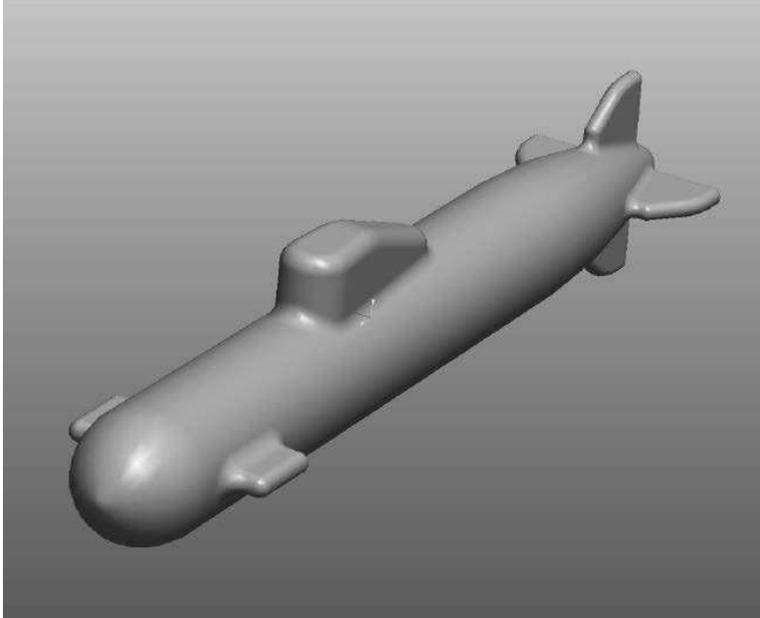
Geometrie des U-Bootes in Pro/ENGINEER
